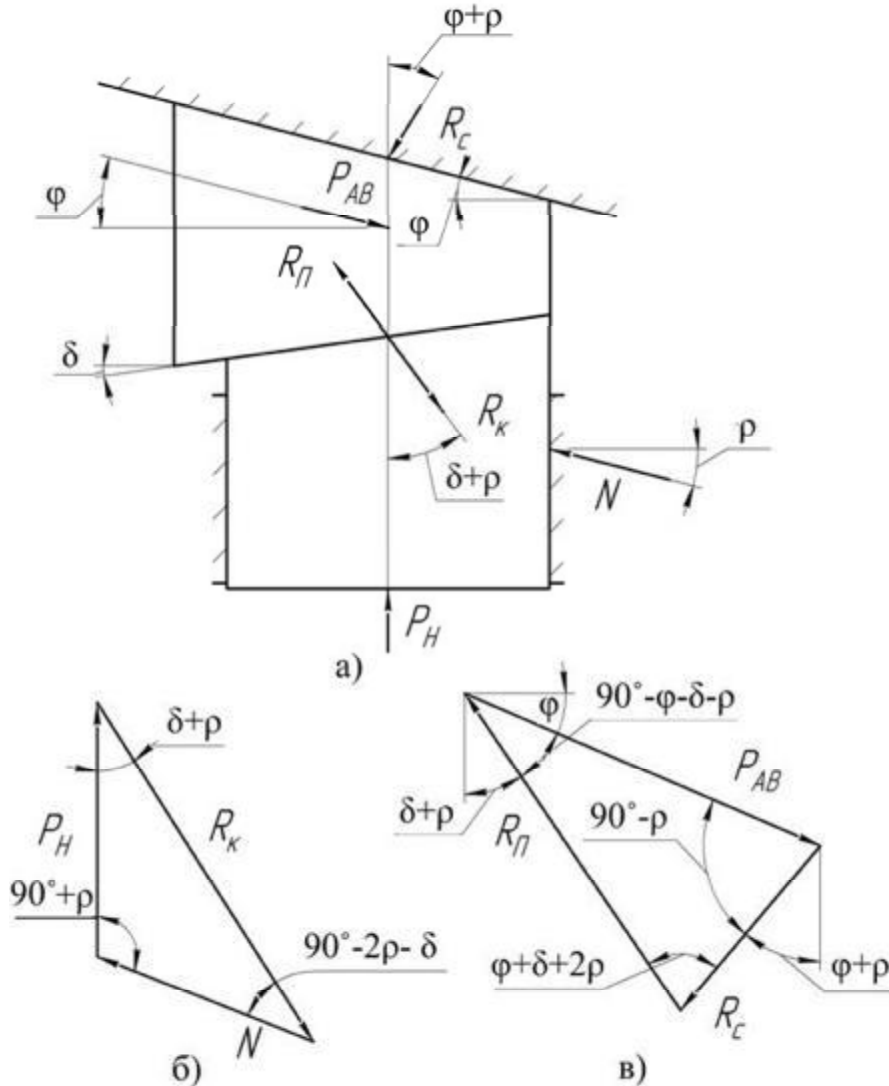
Розрахункова схема зусиль, якими навантажені повзун і клин при штампуванні заготовки
